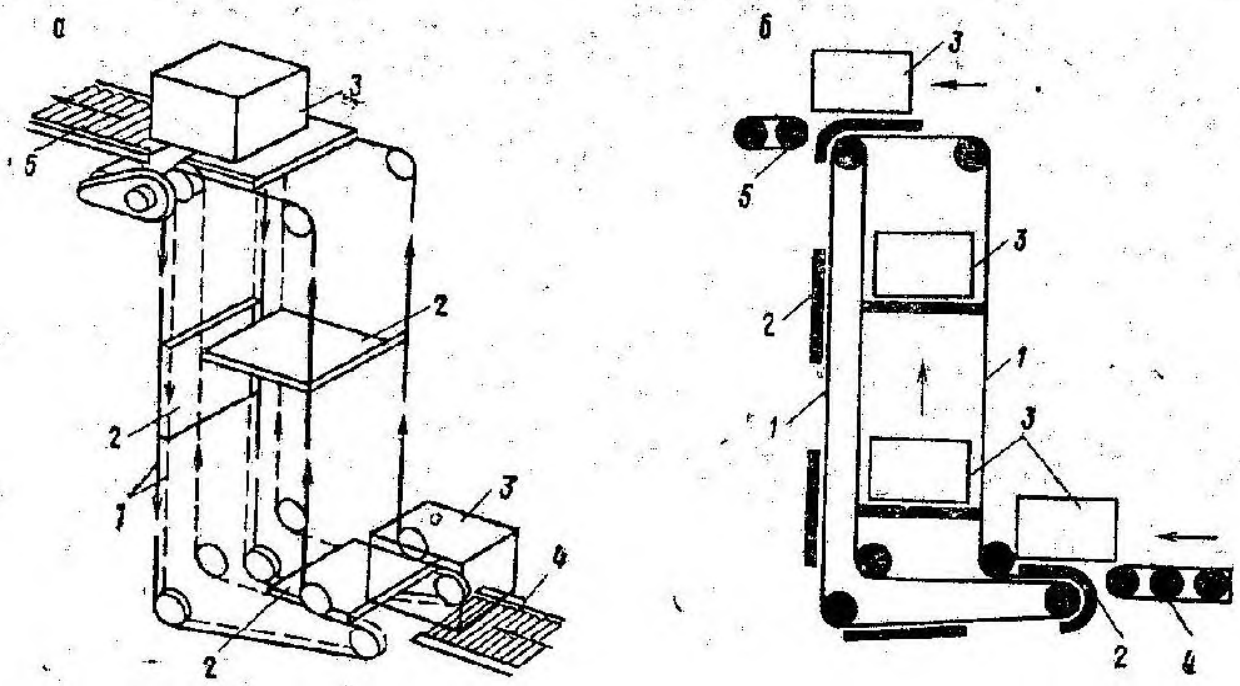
Схема элеватора-конвейера для подъема и спуска кип целлюлозы и стоп бумаги:
